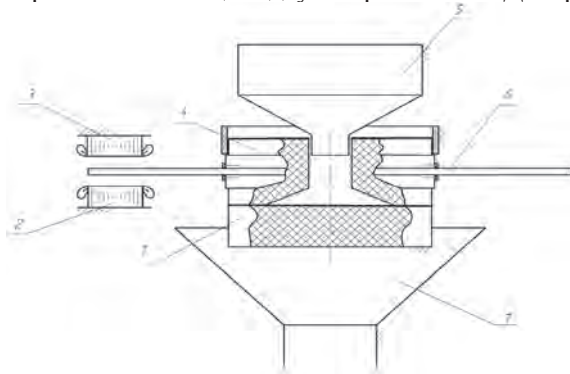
Кинематическая схема жерновой мельницы с двухсторонним ЛАД в приводе: 1 – нижний неподвижный жернов; 2, 3 – индукторы ЛАД; 4 – верхний подвижный жернов; 5 – загрузочный бункер; 6 – вторичный элемент ЛАД; 7 – разгрузочный бункер
